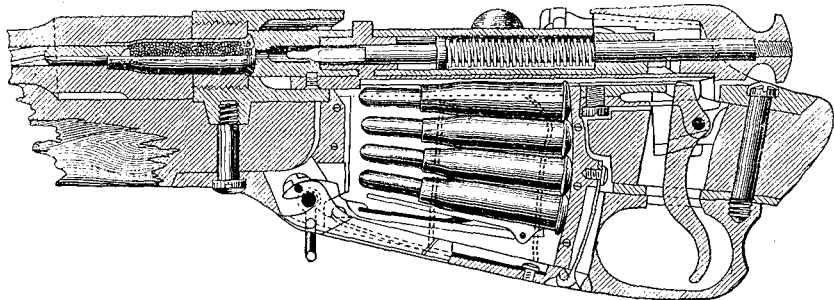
Механизм советской винтовки образца 1891/1930 гг. (затвор, патронник, магазинная коробка).
